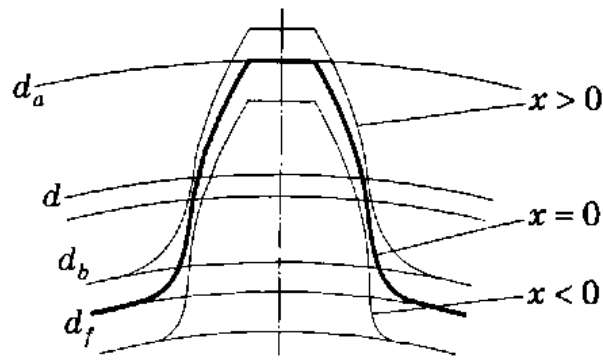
Профиль зубьев, изготовленных с разным смещением
